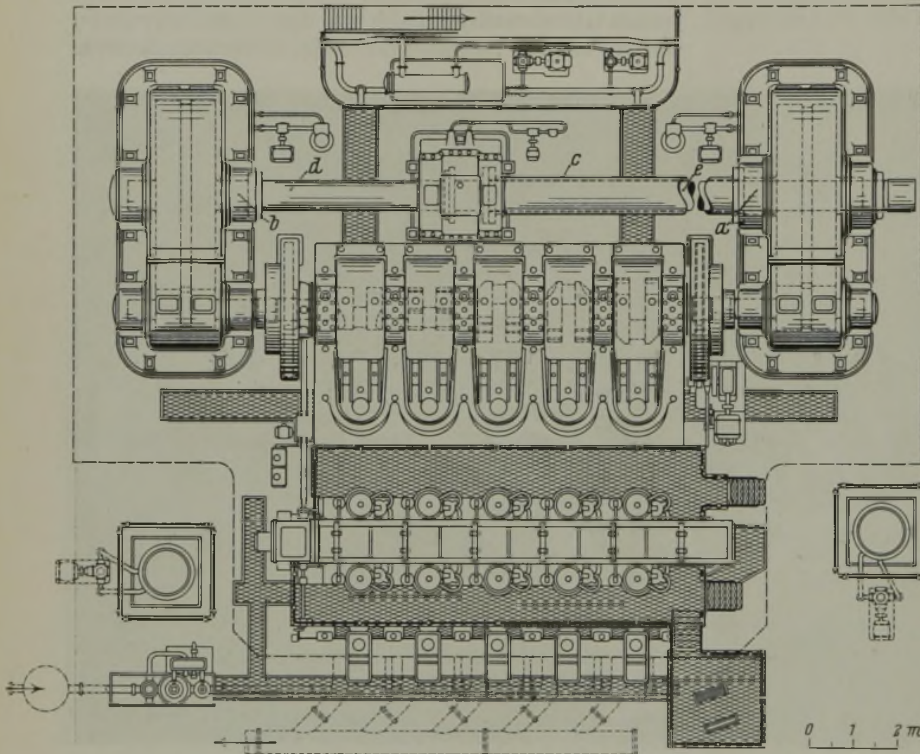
Fünf-Zylinder-Umkehrdampfmaschine, Anlageplan.
